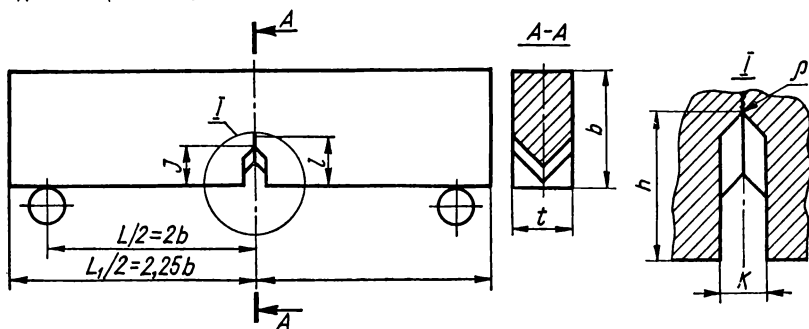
Образец для испытаний на сосредоточенный изгиб:
